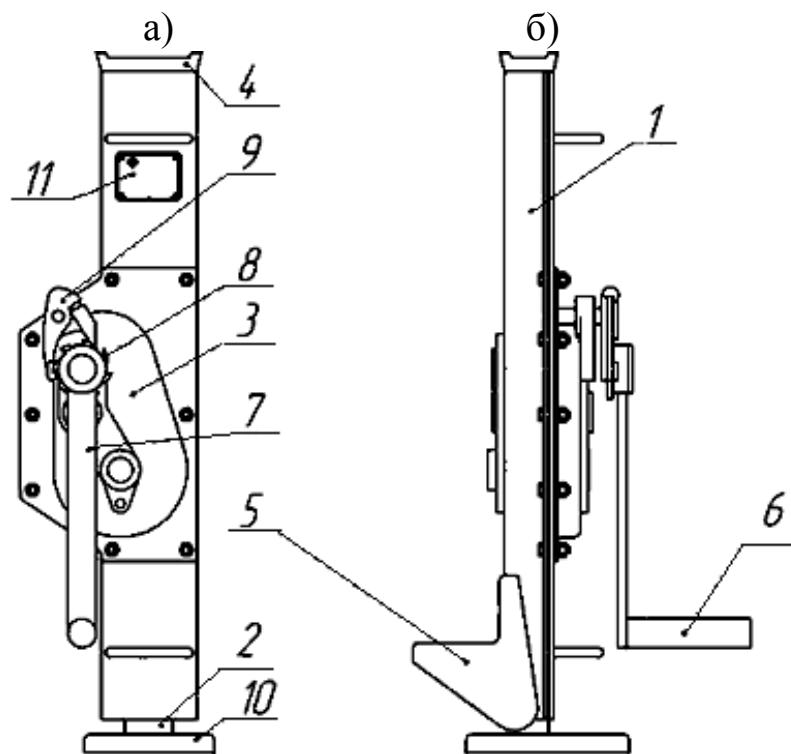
Домкрат реечный зубчатый: а – общий вид; б – принципиальная схема; 1 – корпус; 2 – рейка; 3 – крышка; 4 – головка; 5 – лапа; 6 – держатель; 7 – рукоятка; 8 – храповик; 9 – собачка; 10 – основание; 11 – табличка
